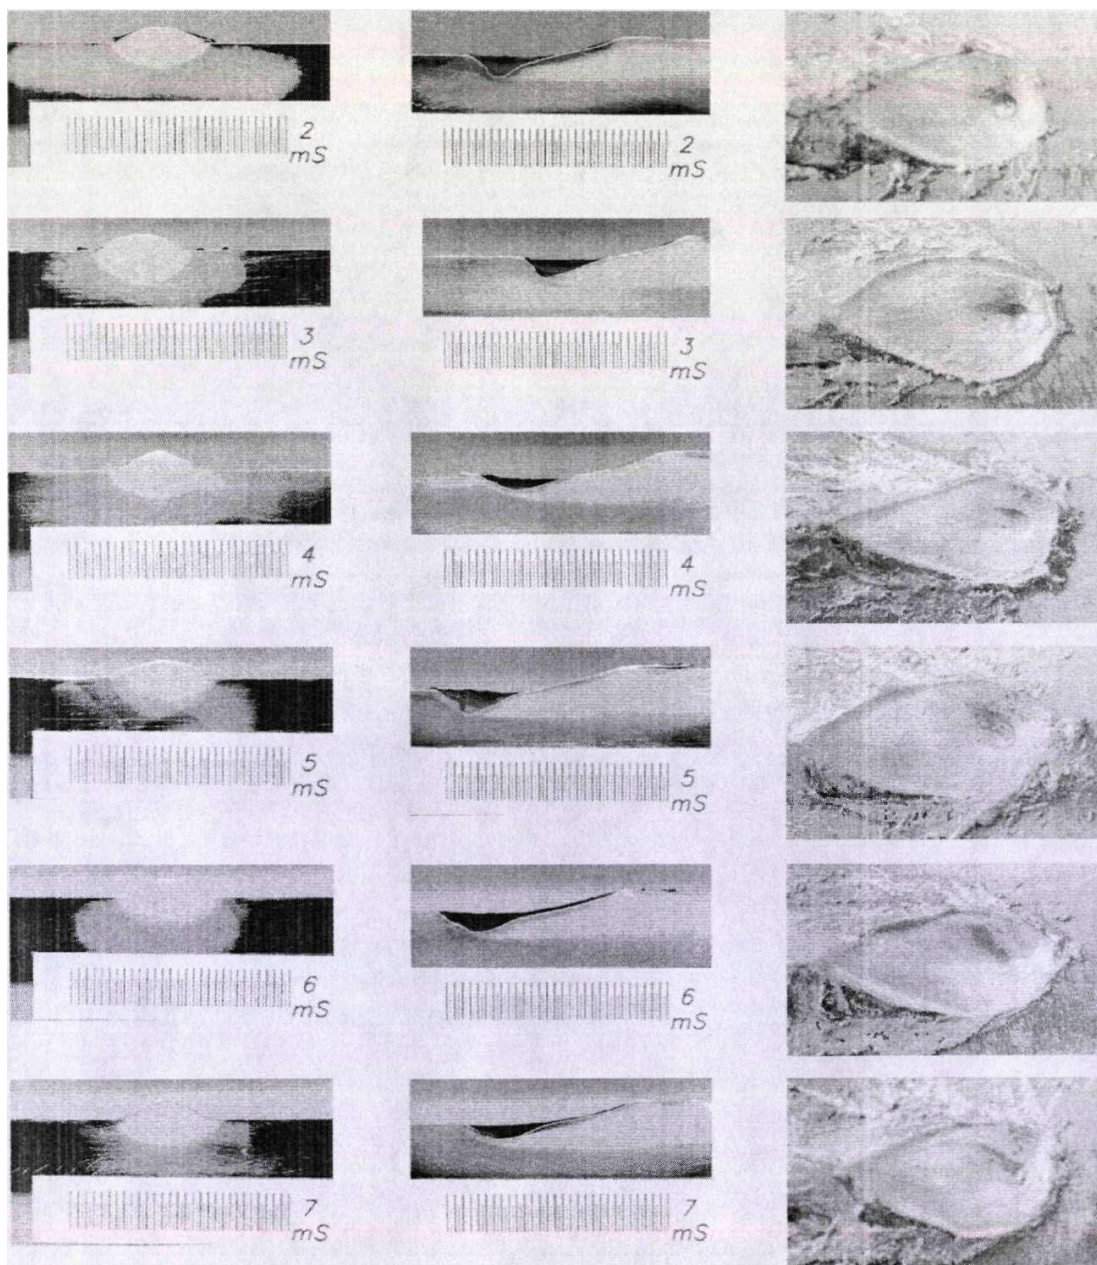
Форма валиков и сварочной ванны с разными значениями длительности импульсов.
